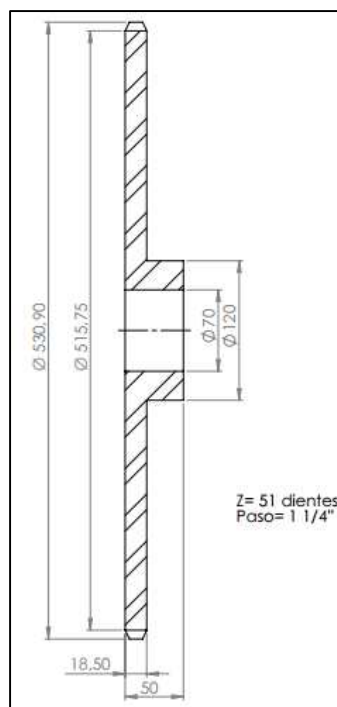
Engranaje de 51 dientes, paso 1 1/4"
